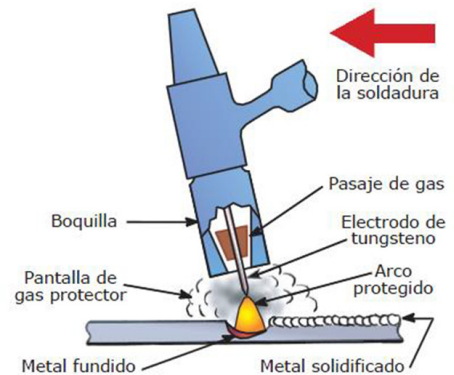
Esquema de funcionamiento del proceso de soldadura por TIG
